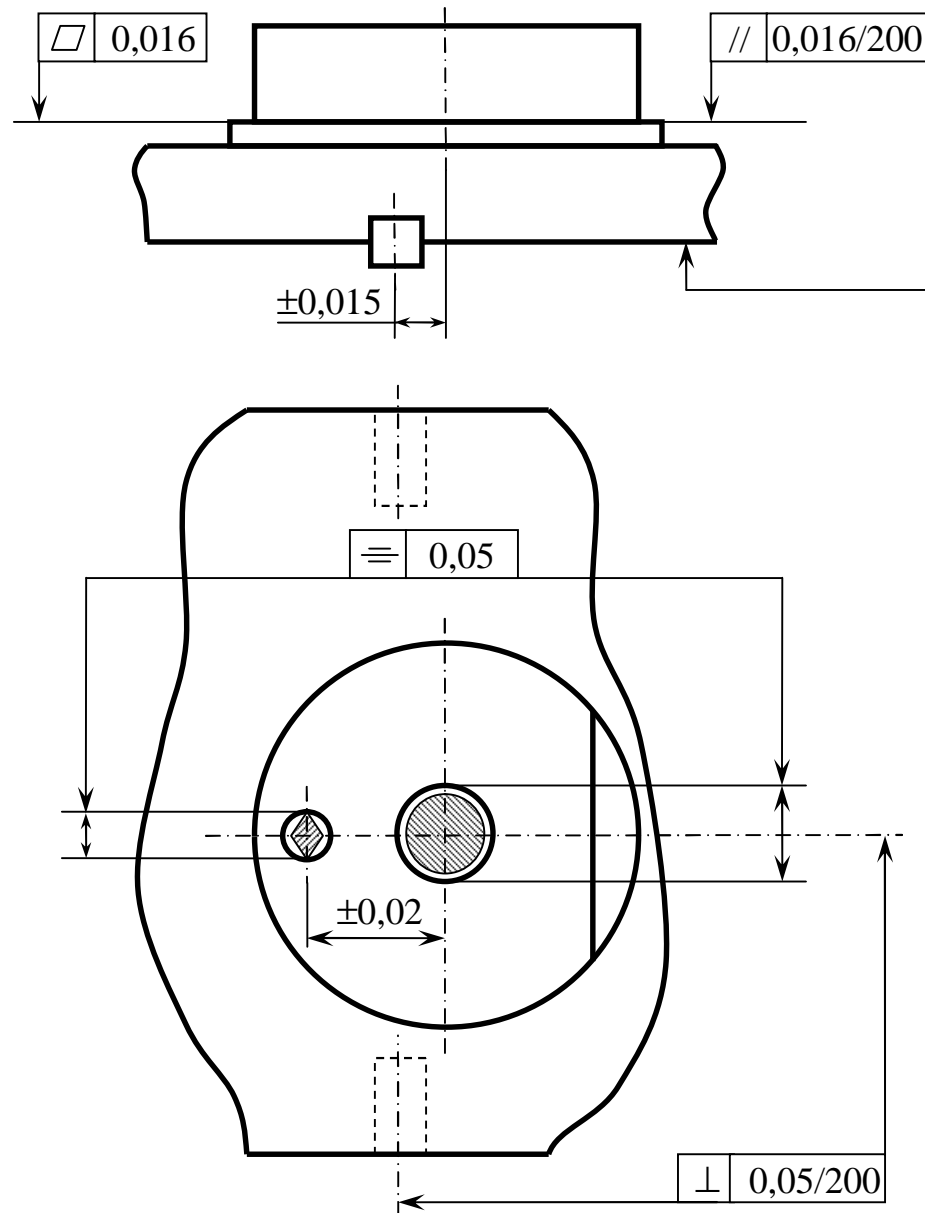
Назначенные допуски формы и расположения в конструкции приспособления
